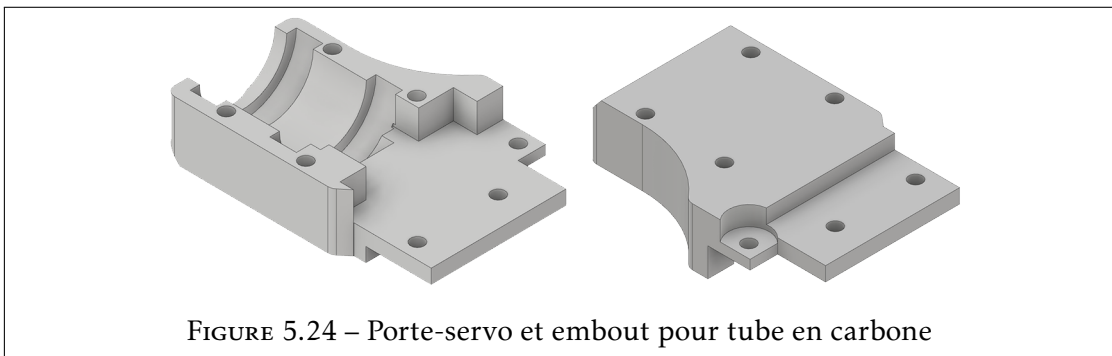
Porte-servo et embout pour tube en carbone
